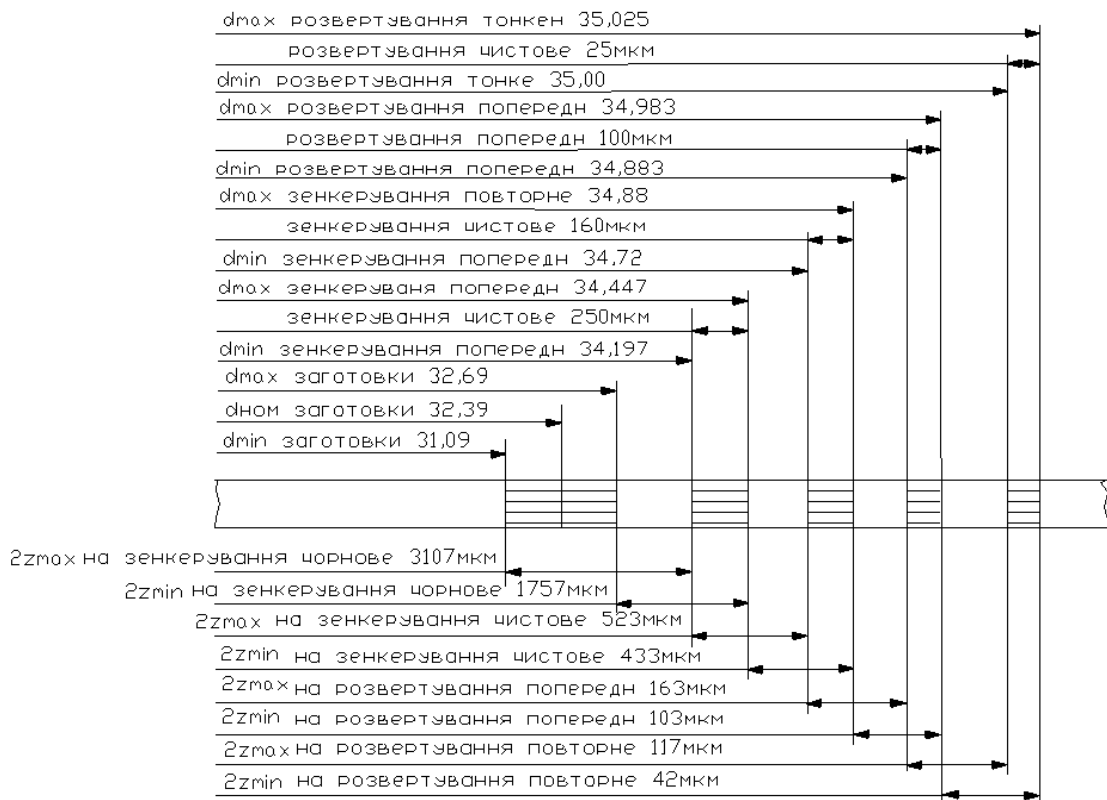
Припуски та допуски на обробку поверхні $\varnothing 35H7$
